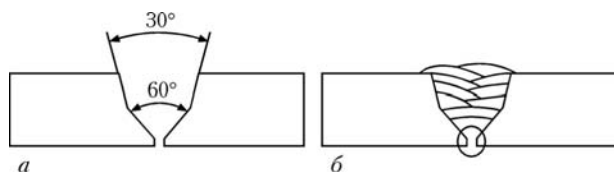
Схема разделки кромок (а) и раскладки швов при многослойной сварке (б)
